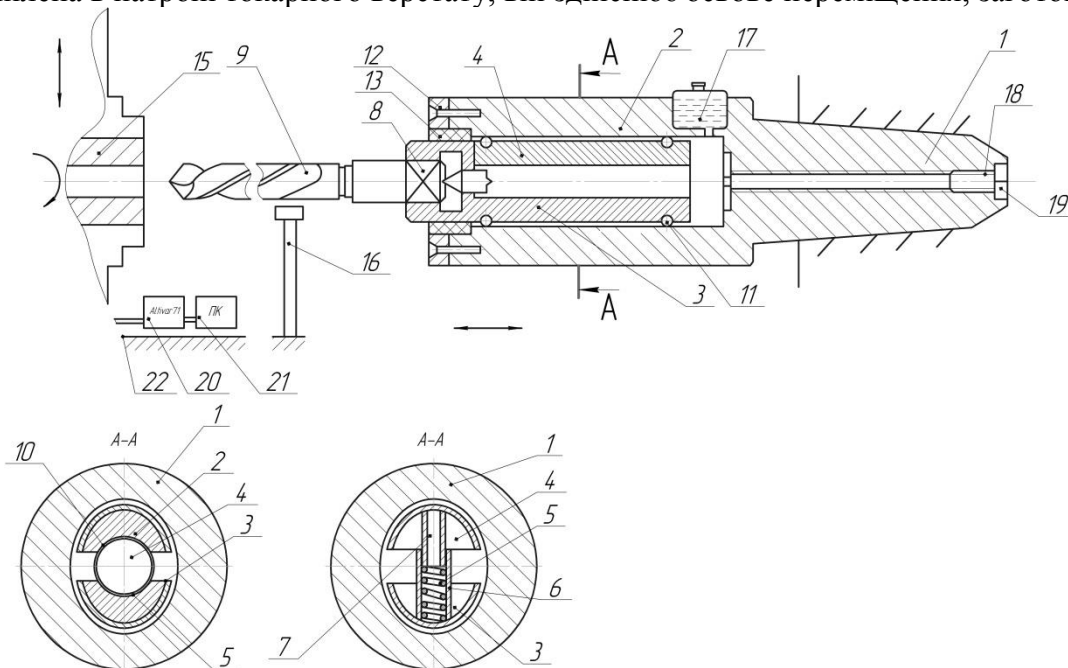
Патрон для оброблення деталей пальцевими ріжучими інструментами
